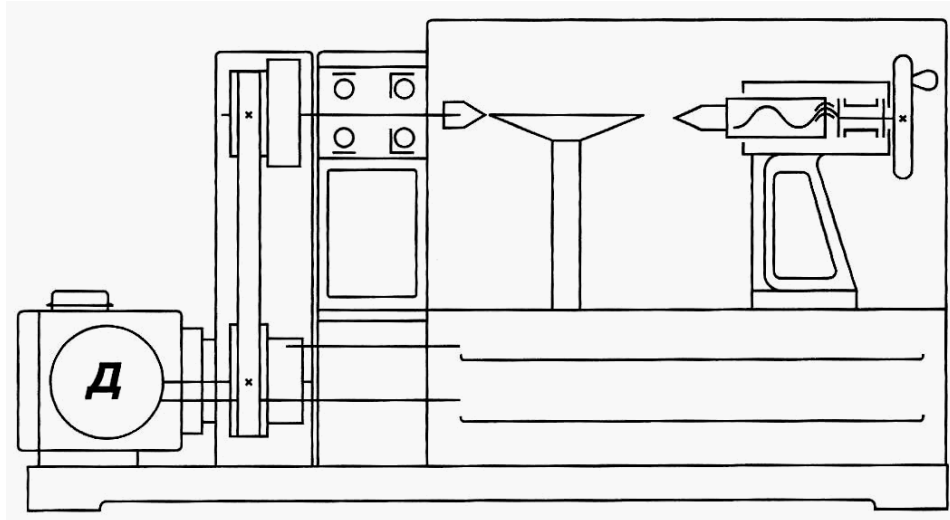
Кінематична схема токарного верстата СТД 120
